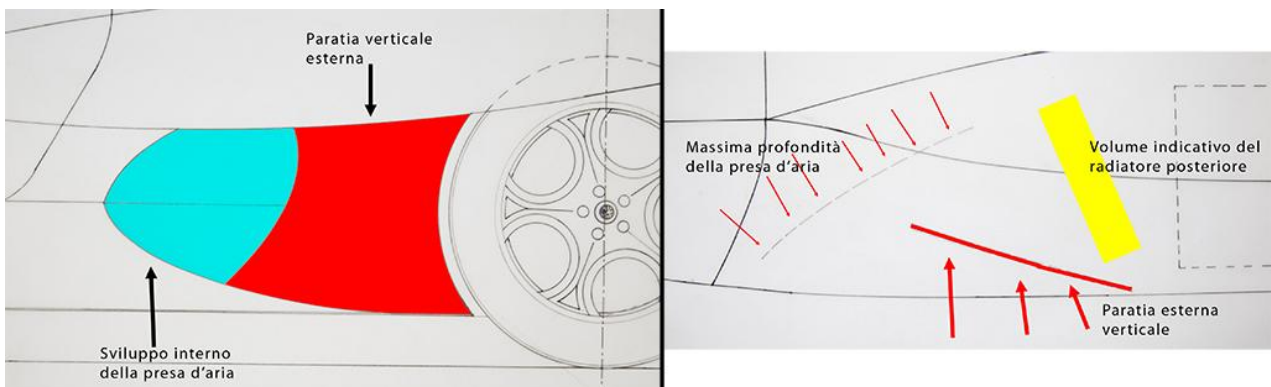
Presa d'aria posteriore raffigurata rispettivamente sul fianco e in pianta
